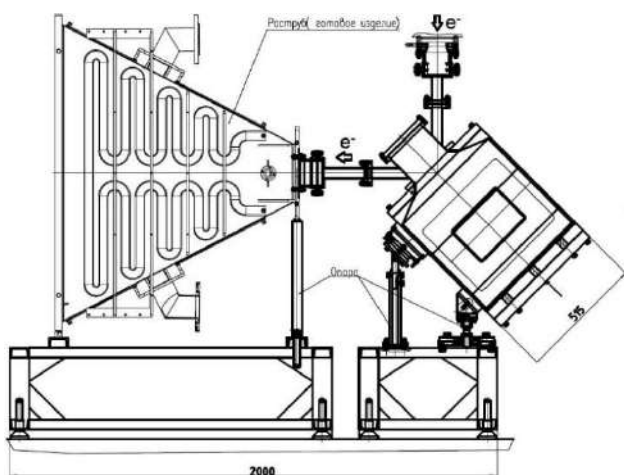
Общий вид разрабатываемой системы поворота и выпуска пучка.
